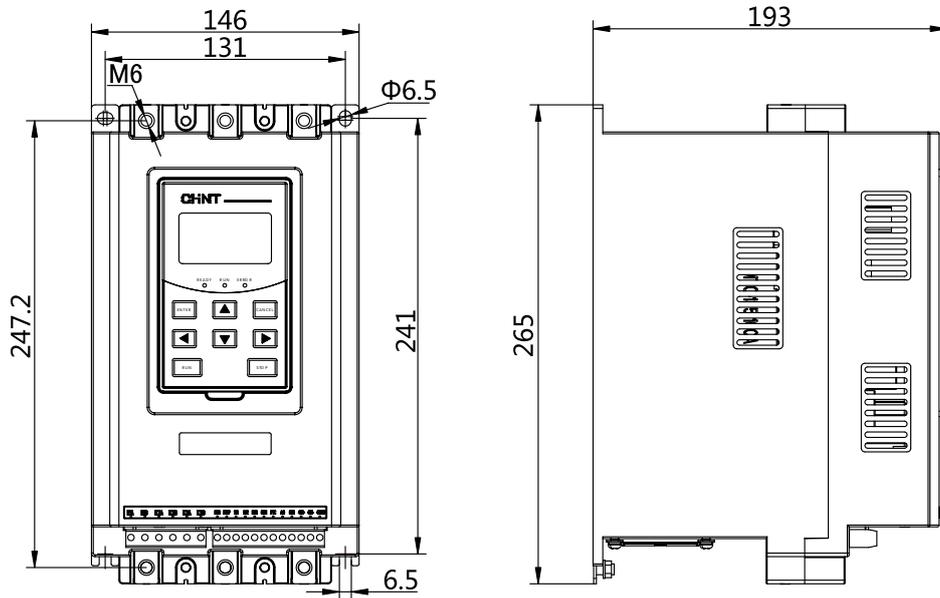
Общий компоновочный и установочный габаритный чертеж для устройств моделей NJR5-15/ZX3–NJR5-90/ZX3 и NJR5-15/ZX6–NJR5-90/ZX6
